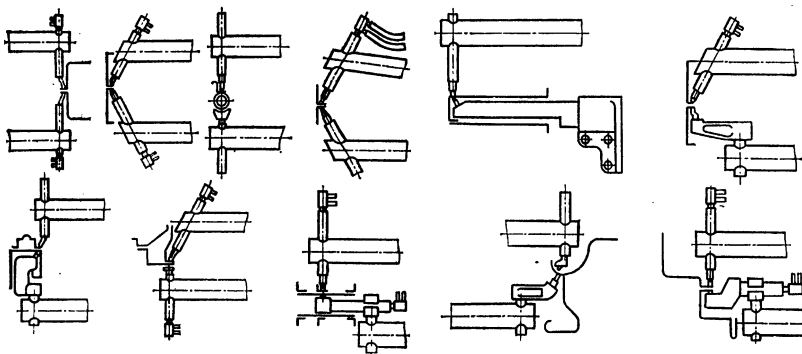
Примеры установки электрододержателей различных типов для сварки в труднодоступных местах
